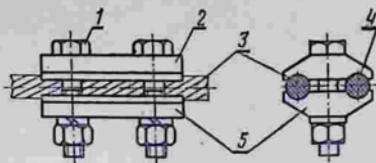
Болтовой плащечный зажим для алюминиевых и сталеалюминиевых проводов:
